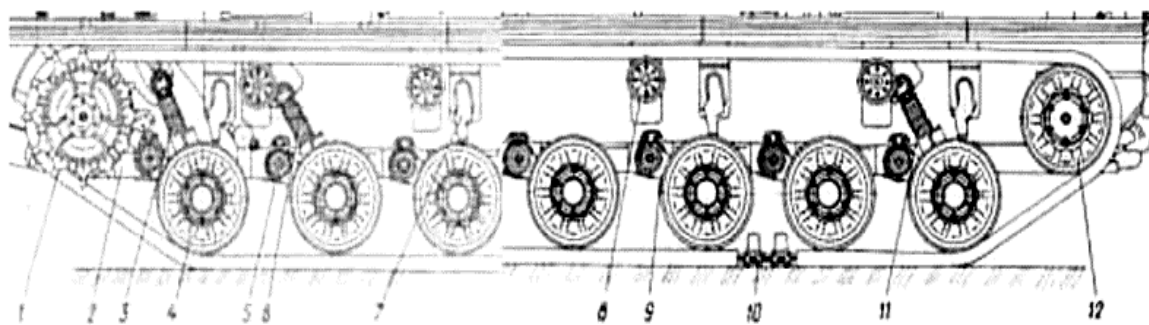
Ходовая часть изделия 453: 1- ведущее колесо; 2 - корпус машины; 3, 6, 11 - гидравлические амортизаторы; 4 - опорный каток; 5 - узел подвески; 7 - упор; 8 - поддерживающий каток; 9 - баланси́р; 10 - гусеница; 12 - направляющее колесо
